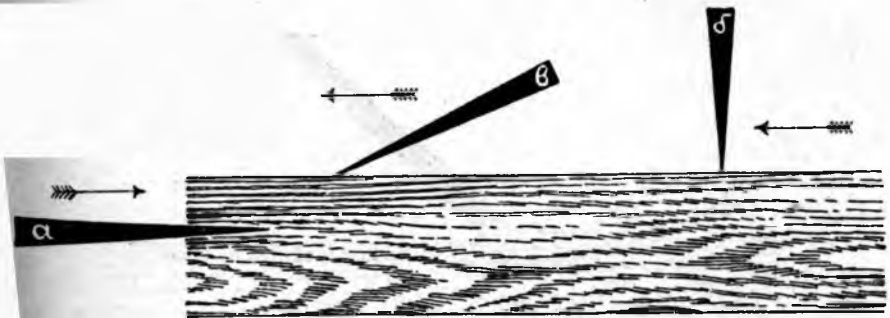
Дѣйствіе обрабатывающихъ инструментовъ: *a* — раскалывающій, *b* — рѣжущій, *c* — скоблящій.
